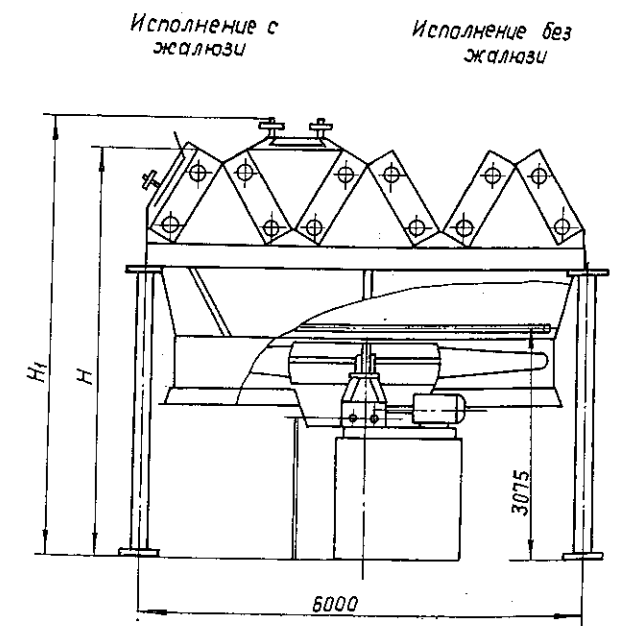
Зигзагообразный аппарат типа АВЗ с металлической опорной конструкцией
